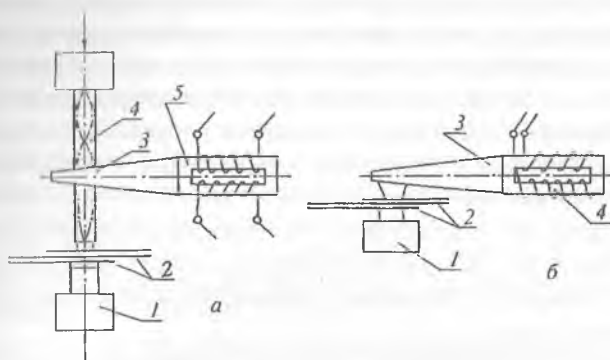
Схемы ультразвуковой сварки: *а* — с поперечным волноводом: 1 — отражатель; 2 — свариваемые листы; 3 — акустический концентратор; 4 — поперечный волновод; 5 — магнитострикционный преобразователь; *б* — с боковым выступом: 1 — отражатель; 2 — свариваемые листы; 3 — акустический концентратор; 4 — магнитострикционный преобразователь
